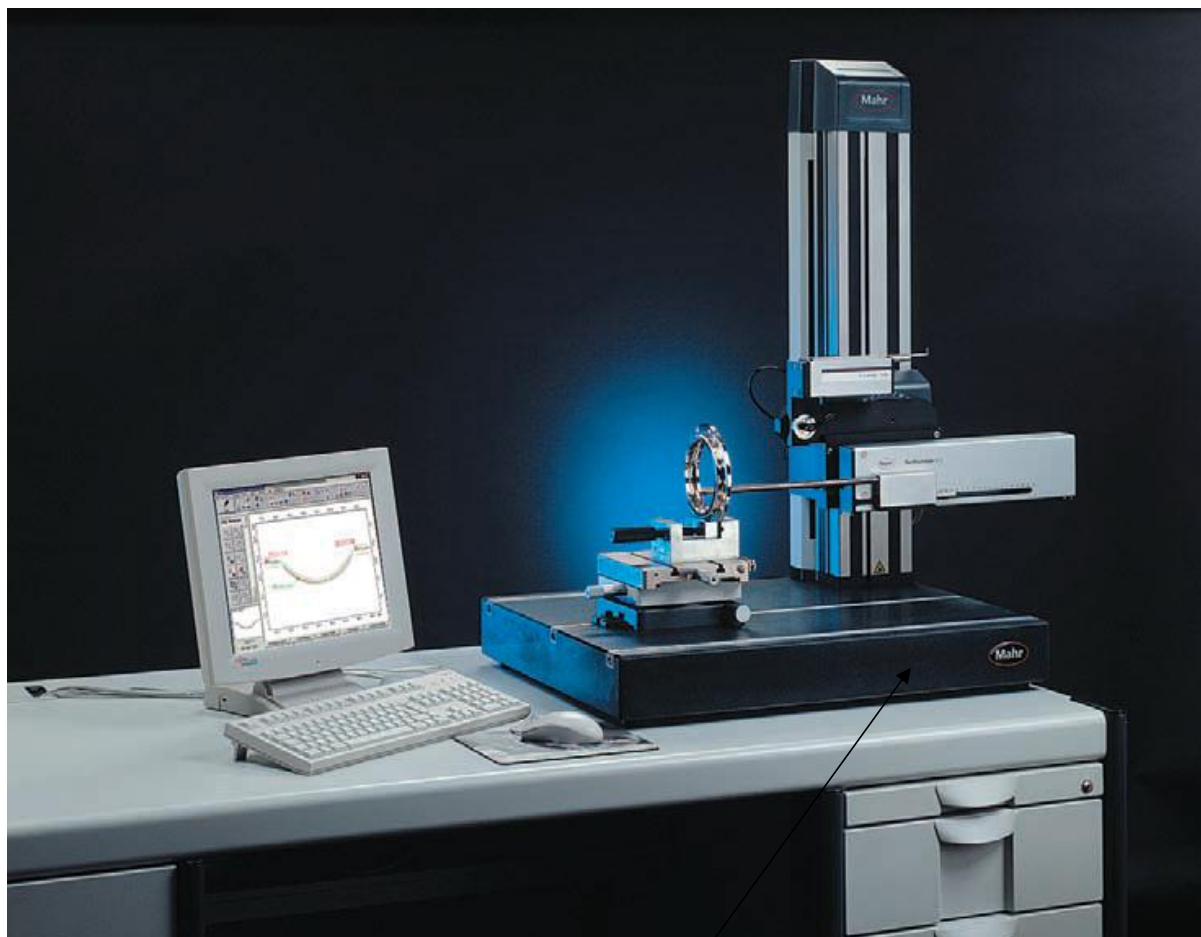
Общий вид приборов для измерений параметров шероховатости и контура поверхности MarSurf XCR 20
